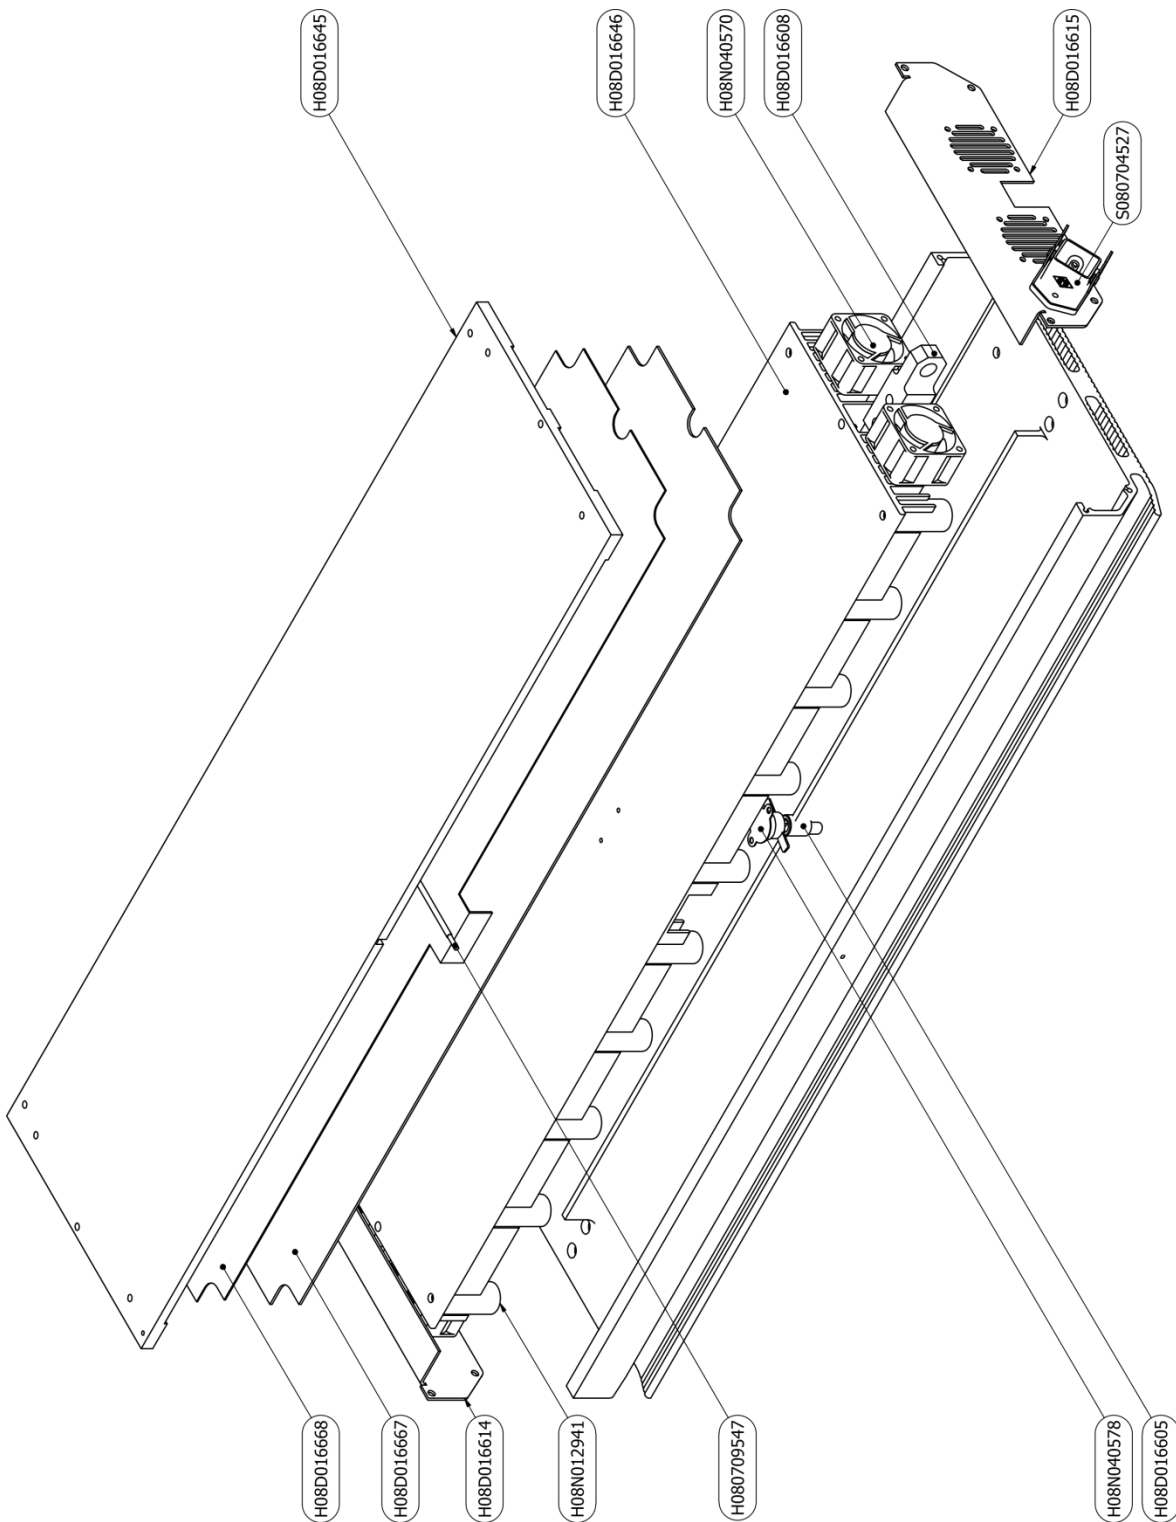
H08D016647 Assemblage de la plaque chauffante inférieure PML-600
